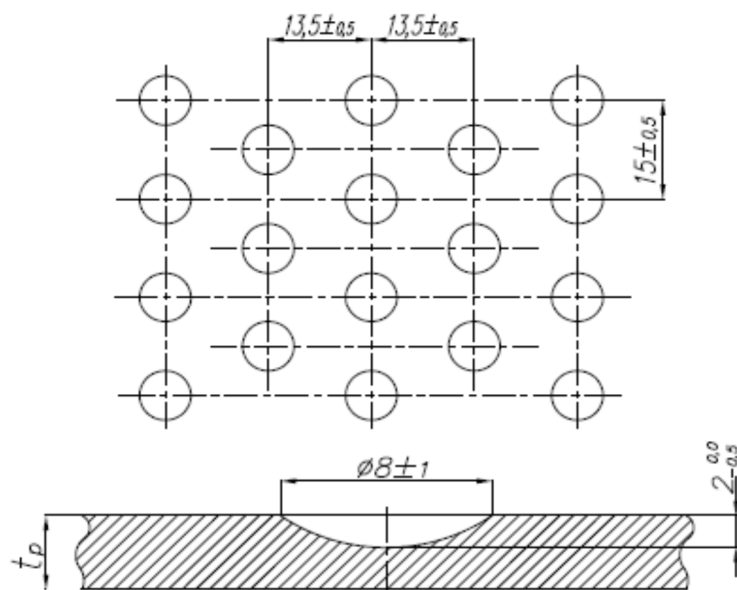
Размеры и расположение углублений (ячеек) для смазки в АП
